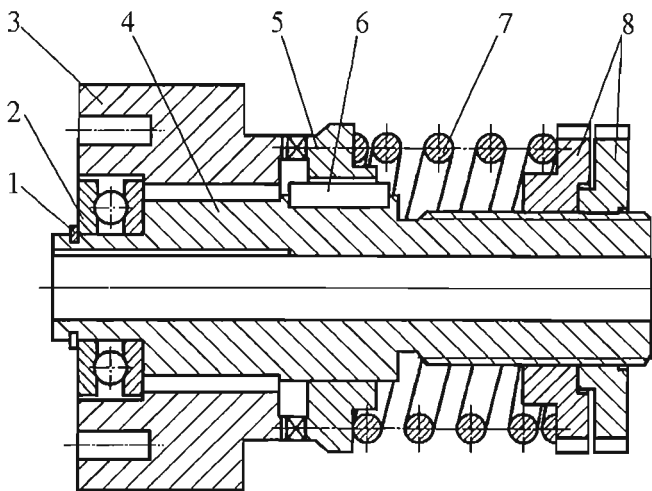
Конструкция кулачковой предохранительной муфты
